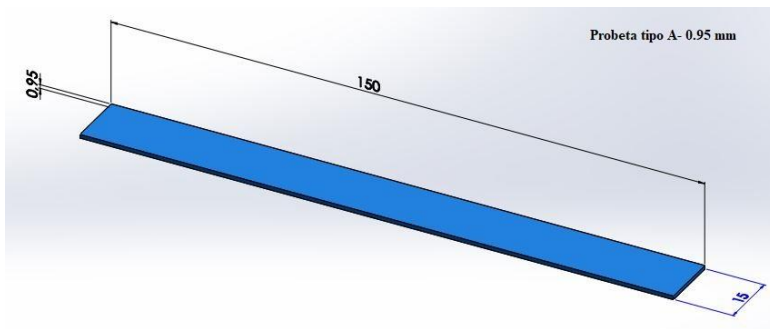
Dimensiones probeta tipo A 0,95 mm de espesor
